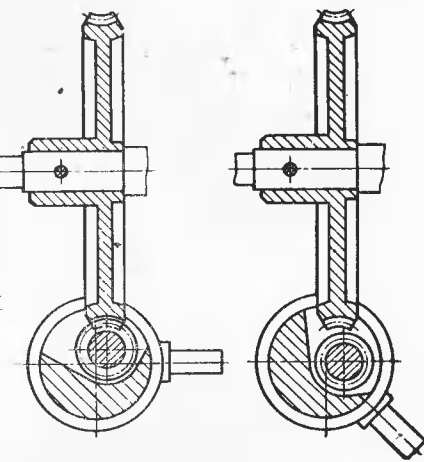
Конструкция червячного зазоровыбирающего механизма с эксцентриковой опорой
